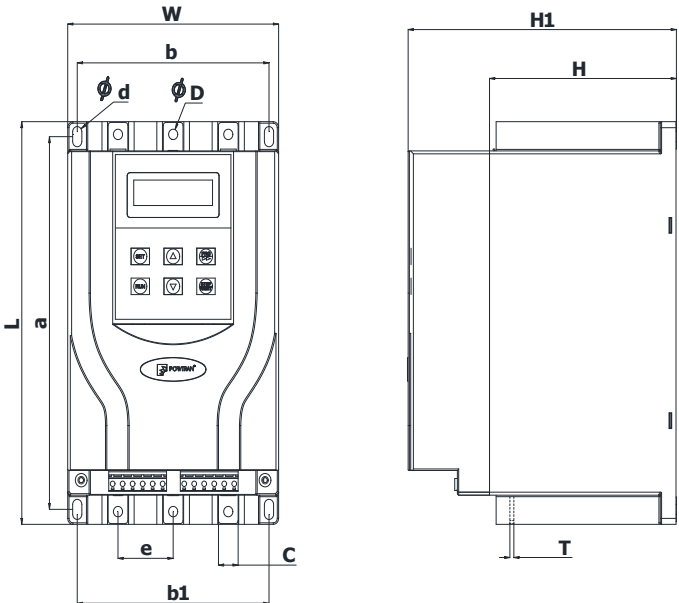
PR5300G3N 11~55kW 外形尺寸 (机座号: F06)
